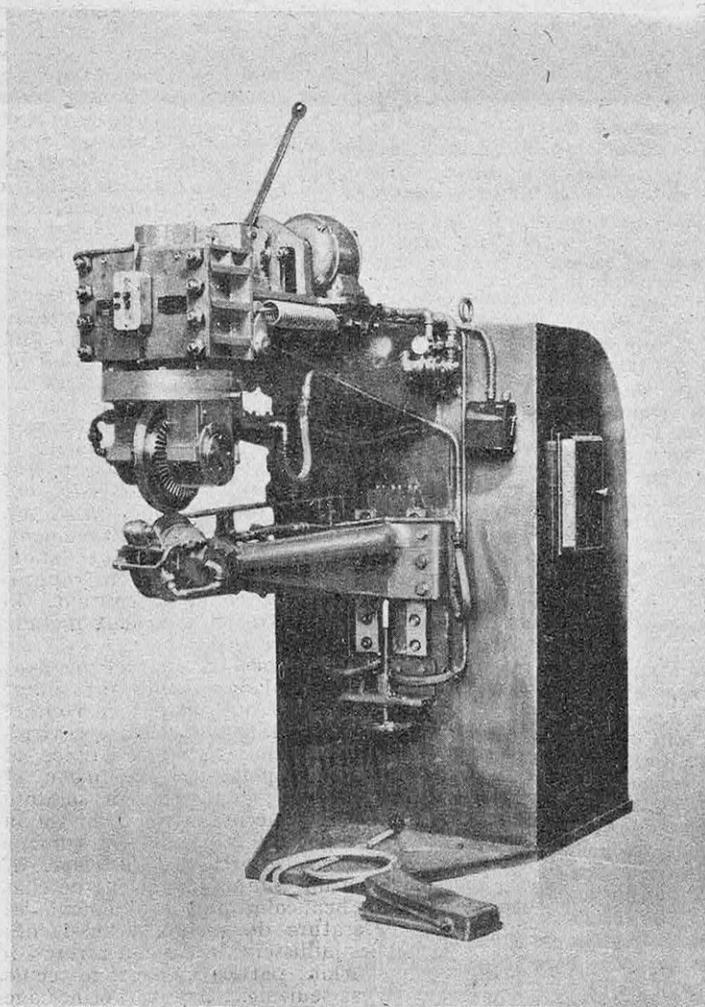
MACHINE A SOUDER A LA MOLETTE PERMETTANT DE RÉALISER DES SOUDURES CONTINUES ÉTANCHES (LA SOUDURE ÉLECTRIQUE)
